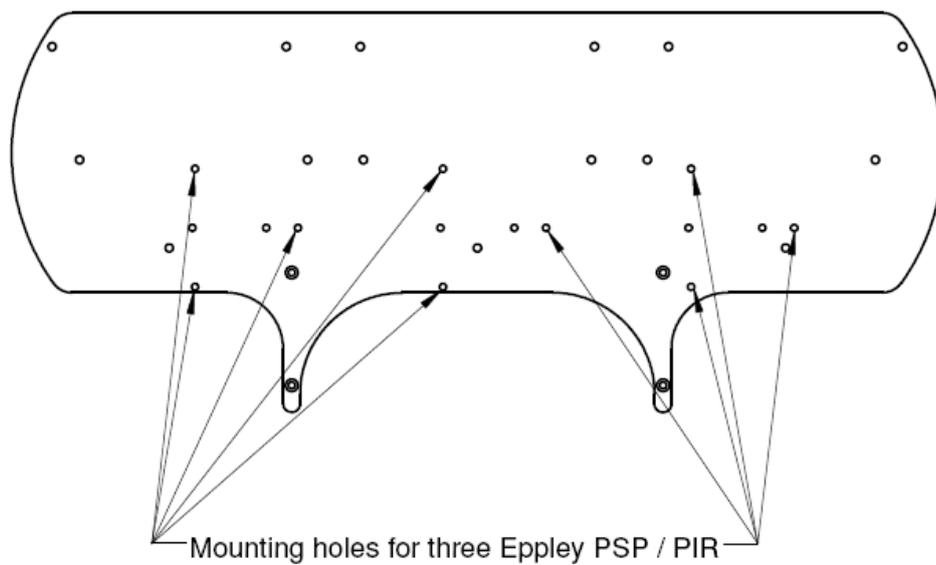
B Montaje de radiómetros Eppley en el Plato de montaje superior
